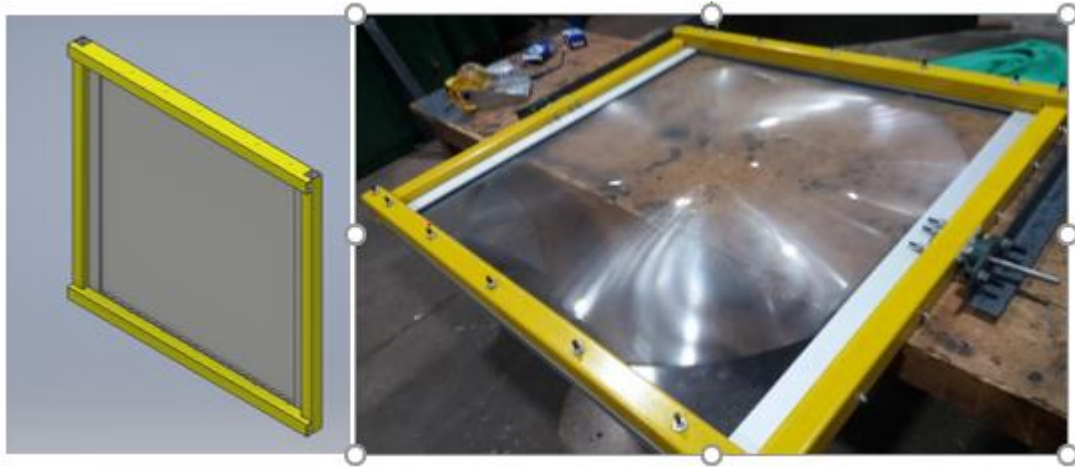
CAD lente enmarcado (izquierda) y elemento construido (derecha).
